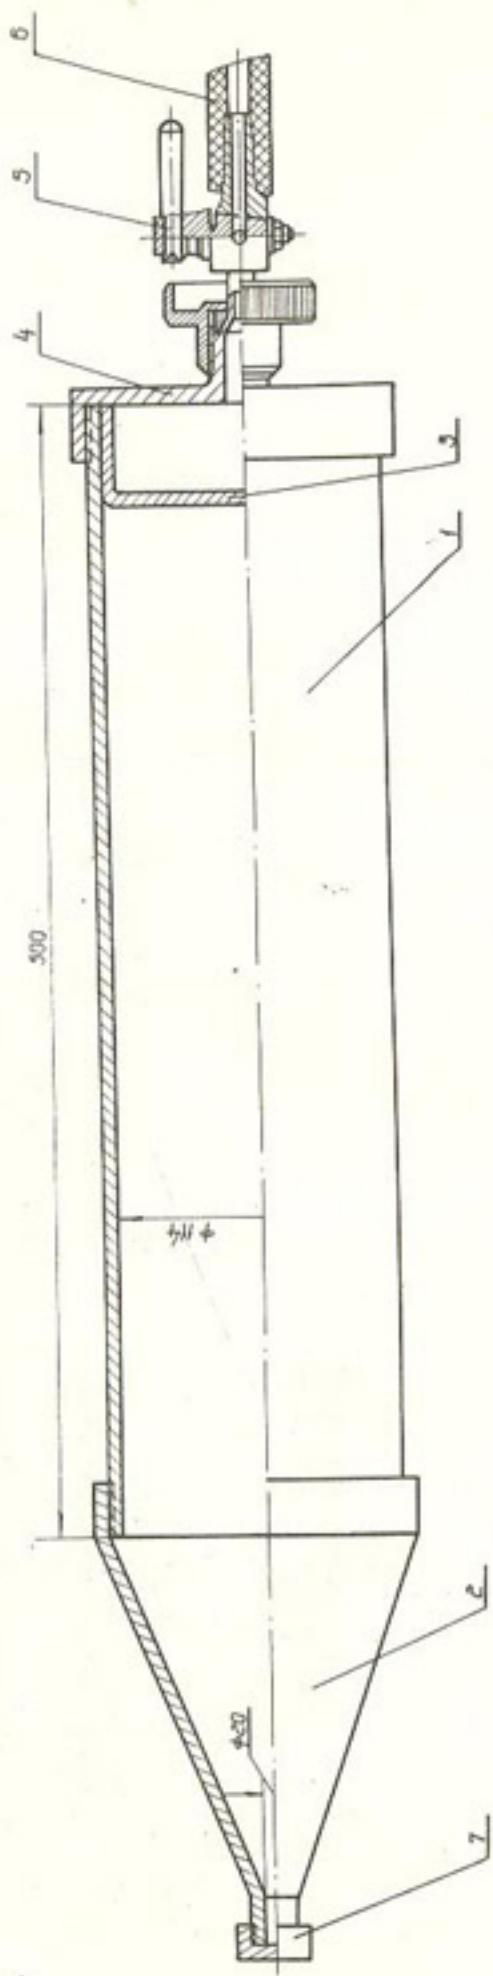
Шприц для нанесения мастики: 1-цилиндр; 2-насадка; 3-поршень; 4-крышка;
